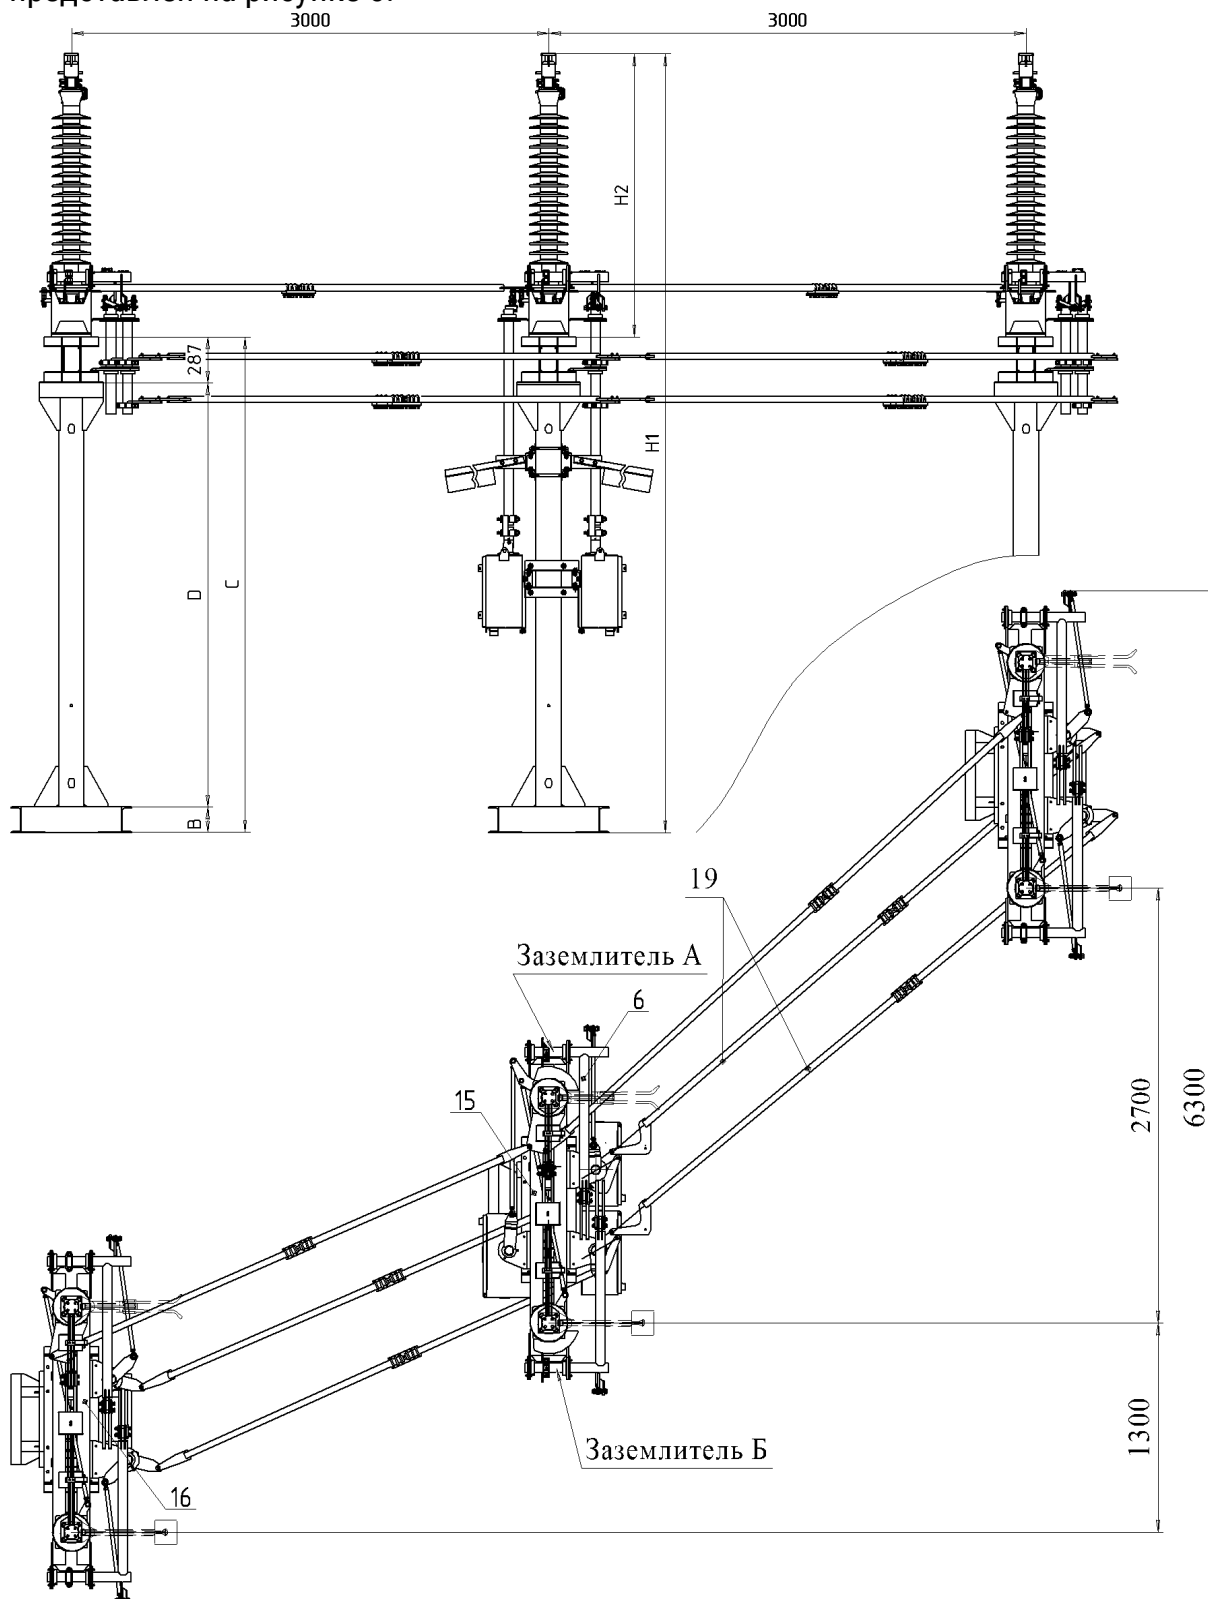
Общий вид ступенчато-килевого разъединителя РНСК СЭЩ®-110
